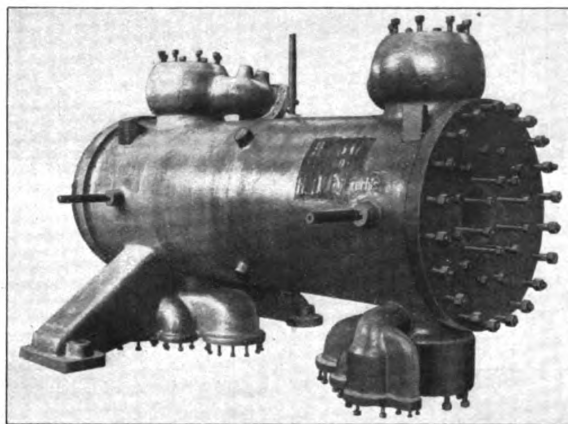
Heißdampf-Zylinder einer Fördermaschine.
